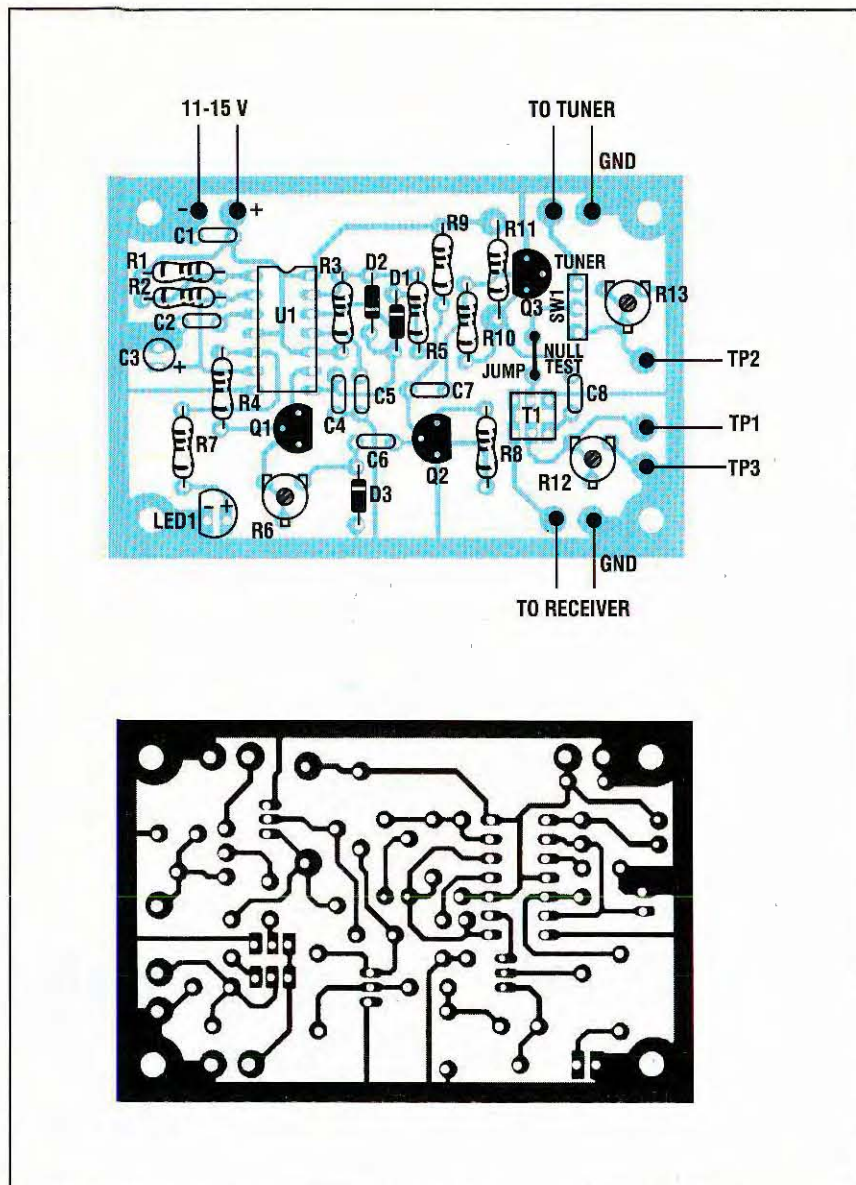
Disegno e piano di montaggio del circuito stampato (in scala 1:1)
